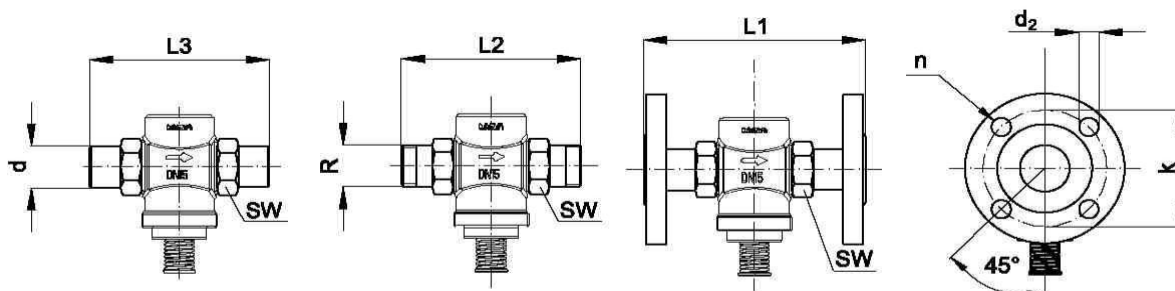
Габаритные и присоединительные размеры регуляторов AVD.
